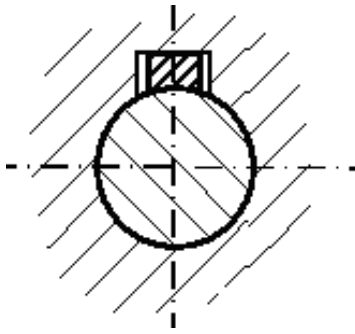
З'єднання деталей за допомогою фрикційної шпонки
